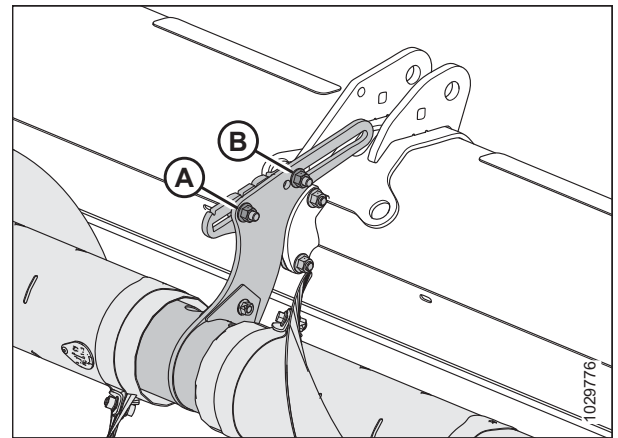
Ursprüngliche Einbaustellung – zweiteilige Schnecke
